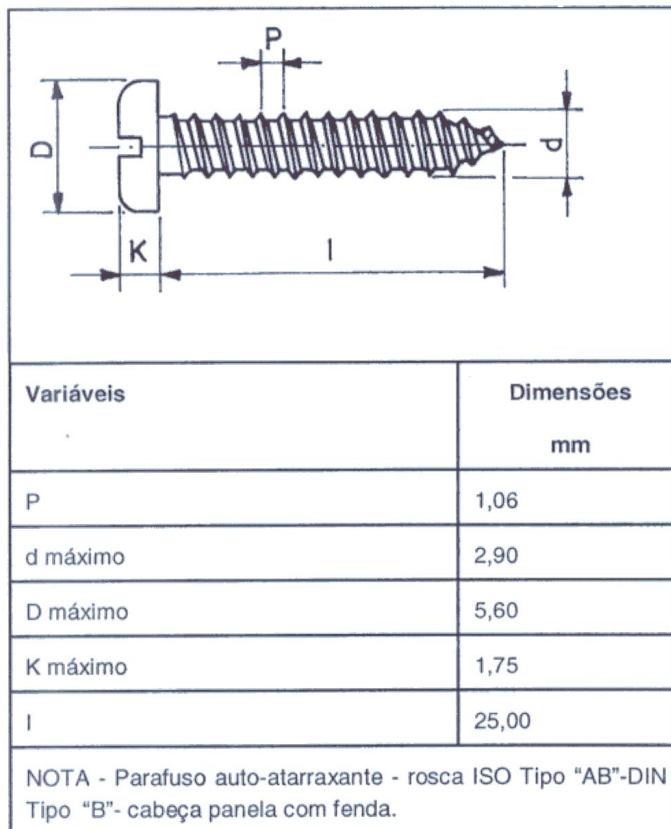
Dimensões e tipo do parafuso a ser utilizado no ensaio.
